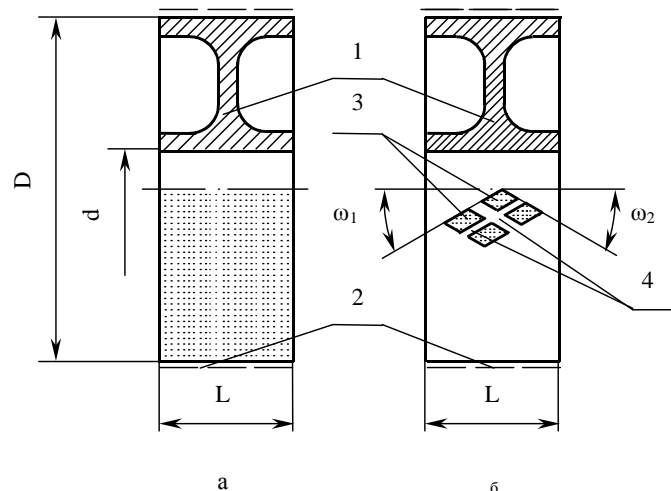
Конструкции однослойного алмазно-абразивного круга со сплошной (а) и прерывистой (б) рабочей поверхностью: 1 – корпус; 2 – алмазодержащий слой; 3 – алмазно-абразивные рабочие элементы; 4 – винтовые канавки левого (n_1) и правого (n_2) направлений
